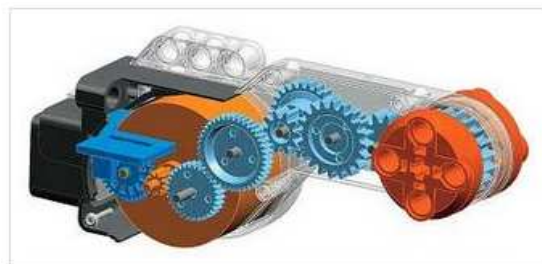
Figura del sistema de engranajes internos del servomotor
